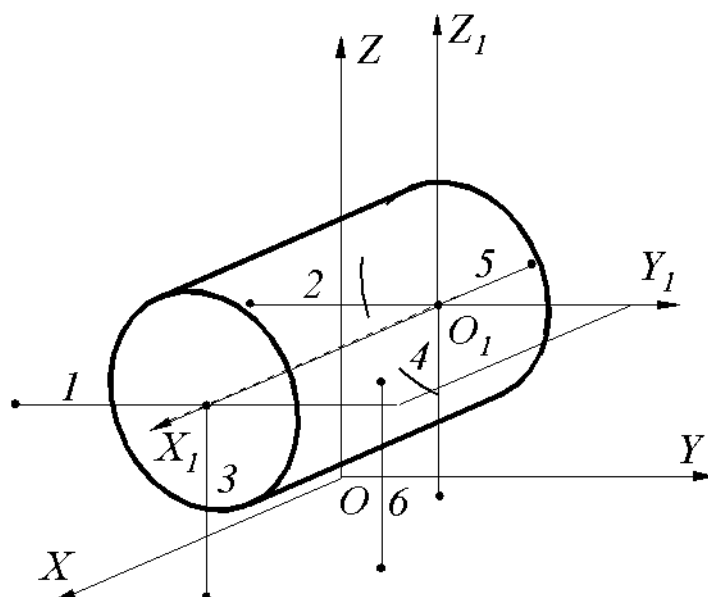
Наложение шести связей на цилиндрическую деталь
